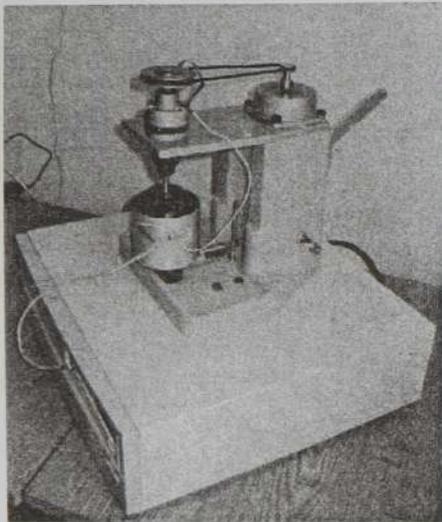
Внешний вид стенда для входного контроля подшипников качения:
